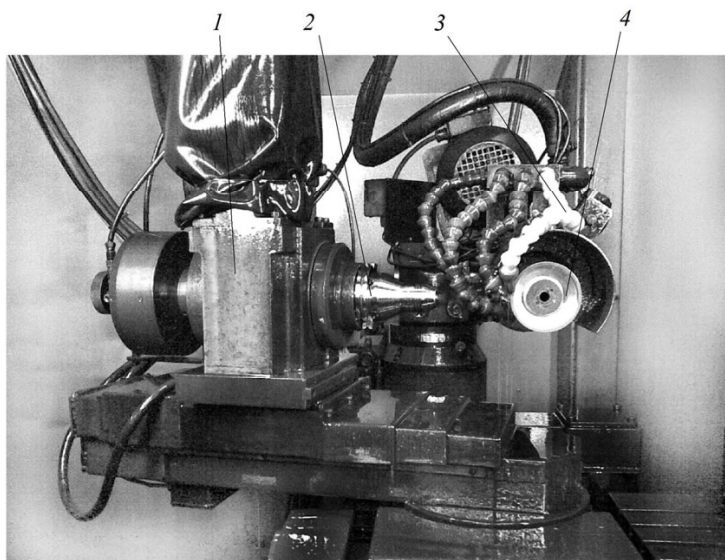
Рабочая зона шлифовально-заточного центра: 1 – передняя бабка; 2 – заготовка; 3 – система сопел для подачи жидкого СОТС; 4 – шлифовальный круг
